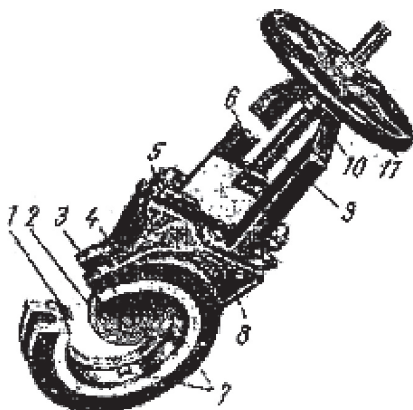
Шиберная задвижка Dezurik: 1 — седло; 2 — шибер; 3 — футеровка; 4 — корпус; 5 — сальник; 6 — бугельная стойка; 7 — направляющая и фиксатор шибера; 8 — ребро жесткости; 9 — шпindel; 10 — ходовая гайка; 11 — маховик
